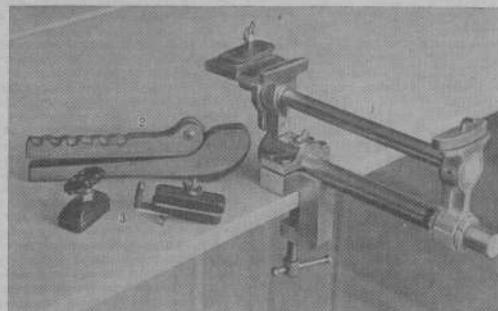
Инструменты и приспособления для натяжки ракеток:
